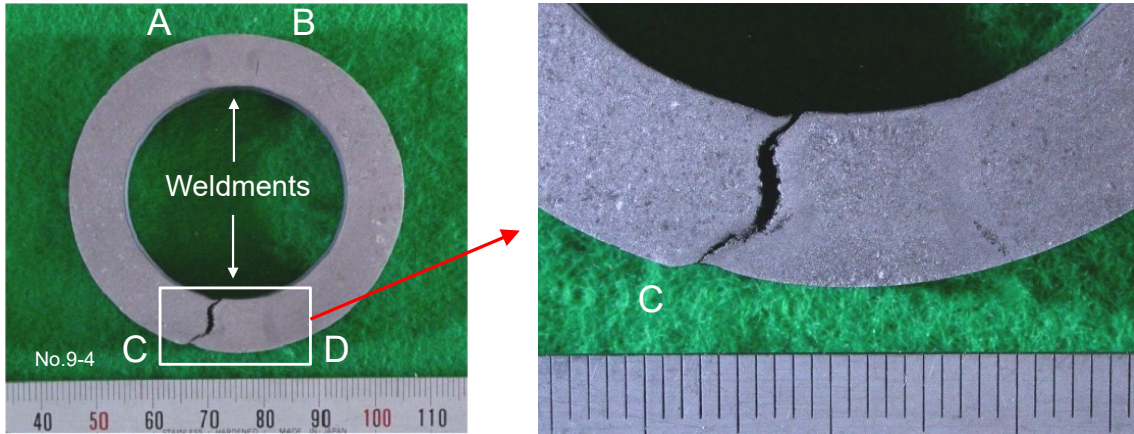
内圧クリープ試験体の破壊後の断面状況(試験体 No. 9-4)
